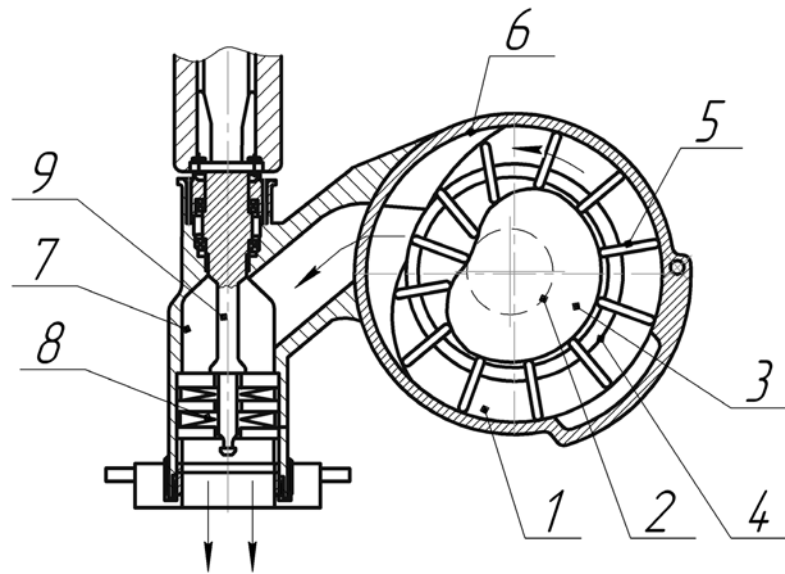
Схема пристрою для подрібнення м'ясної сировини з використанням шприца марки Handtmann VF 628: 1 - корпус фаршевого насоса; 2 - вал; 3 - копір; 4 - ротор; 5 - рухомі лопаті; 6 - внутрішня поверхня корпусу; 7 - горловина; 8 - різальний вузол; 9 - ножовий вал
